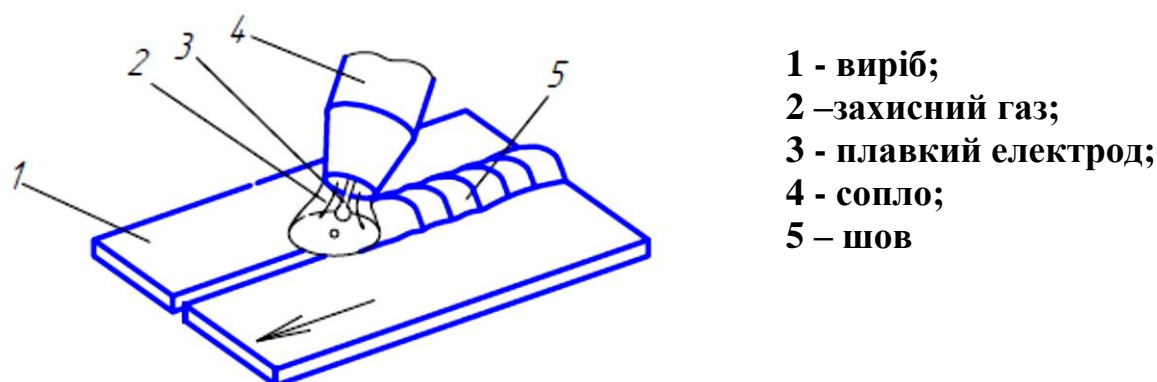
Схема процесу зварки у середовищі захисного газу [6]
